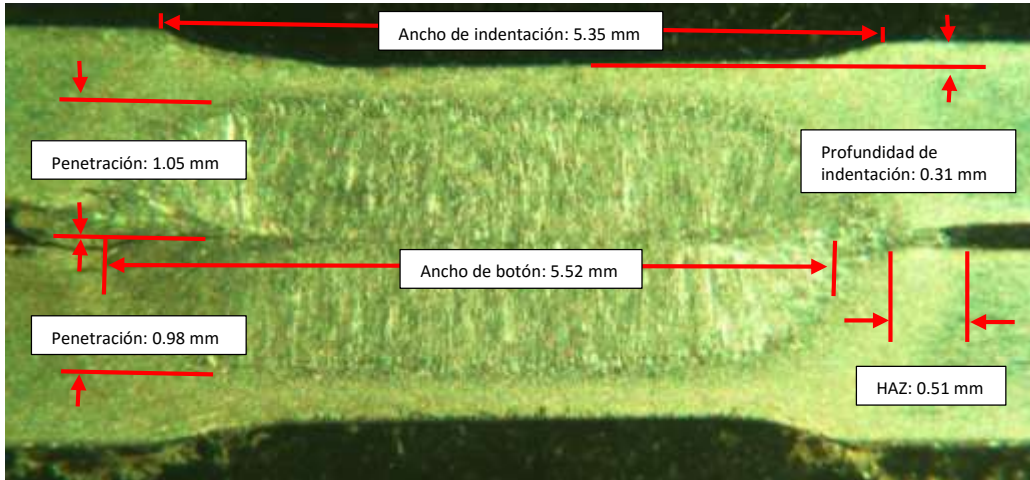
Mediciones realizadas en el botón de soldadura número 17.
